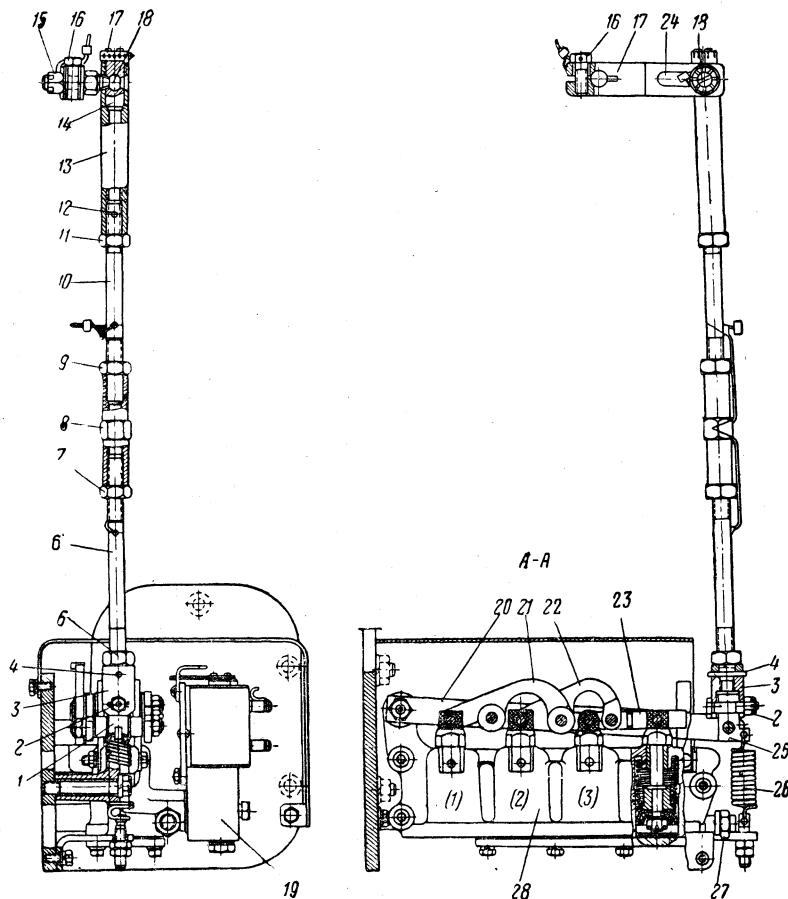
Электропневматический механизм и рычажная передача управления регулятора дизеля 2Д100:
